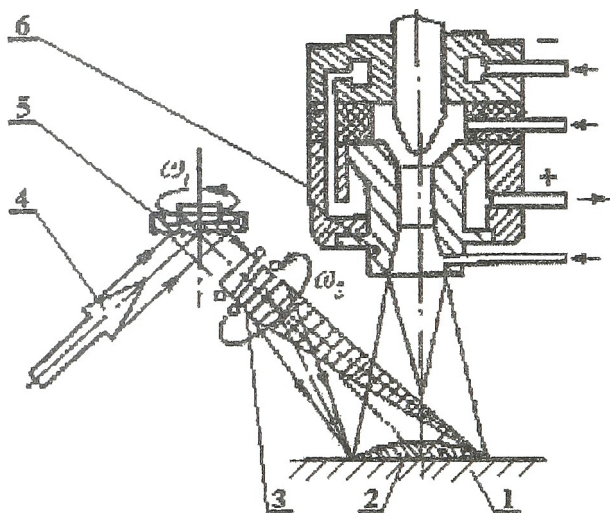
Схема лазерно-плазменного нанесения покрытия.
